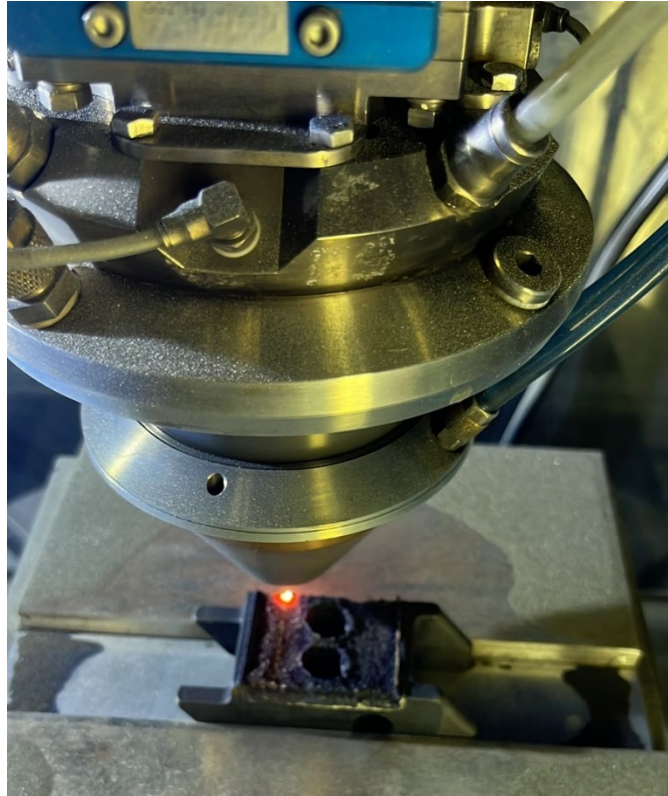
Наплавка порошка ПМС-М99,9 на литой стальной корпус
